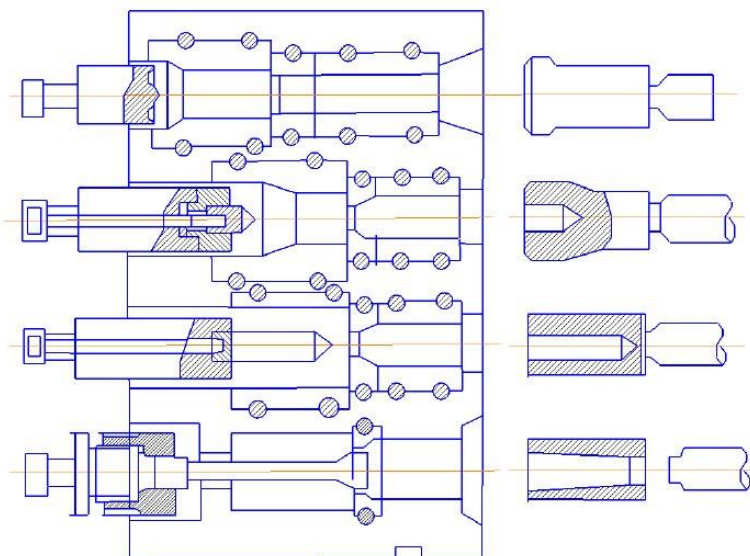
Штамп ГKM для виготовлення поковки типу втулки і переходи штампування
